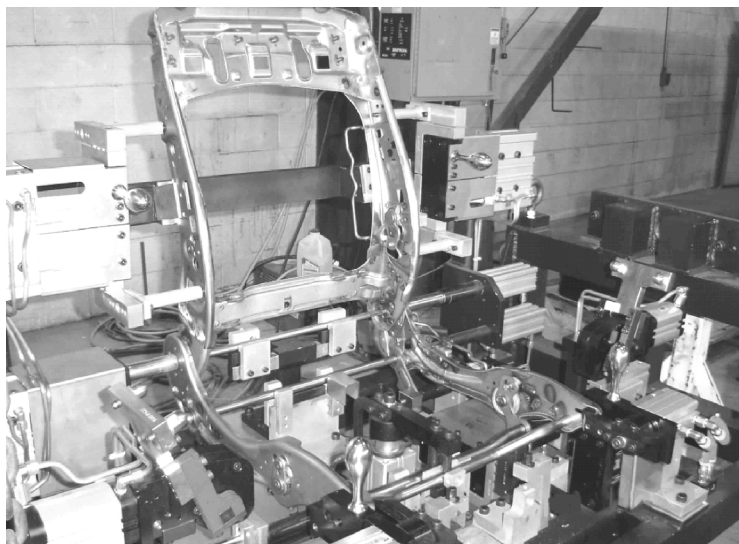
用于汽车车身零部件的焊装夹具
